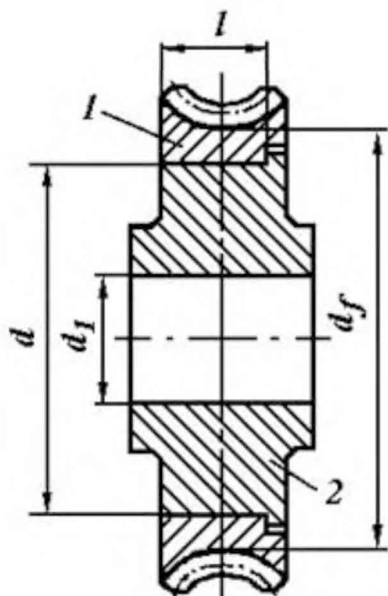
Цилиндрическое соединение с натягом венца червячного колеса с центром
